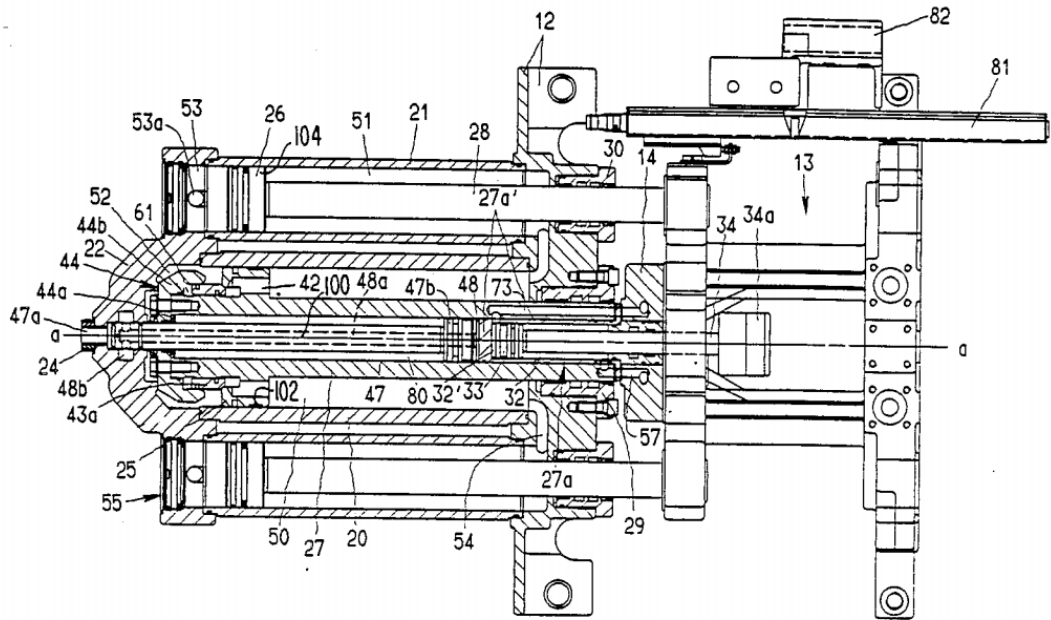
Patent, Gas nozzle for a gas assisted injection molding system
